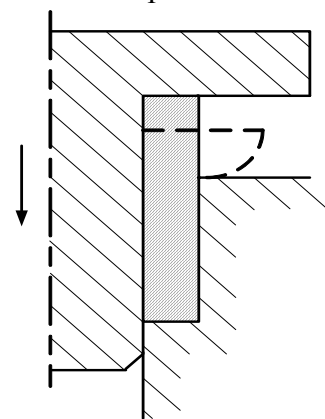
Схема высадки подвижным пуансоном трубной заготовки, установленной в неподвижной матрице
